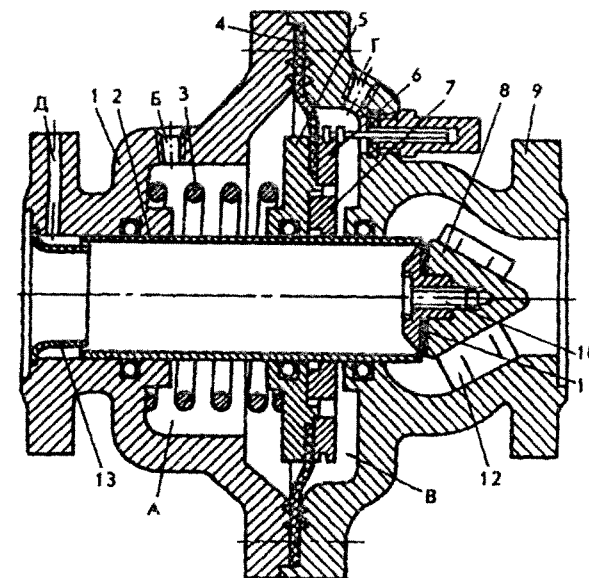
Исполнительное устройство регулятора давления газа РДУ:
